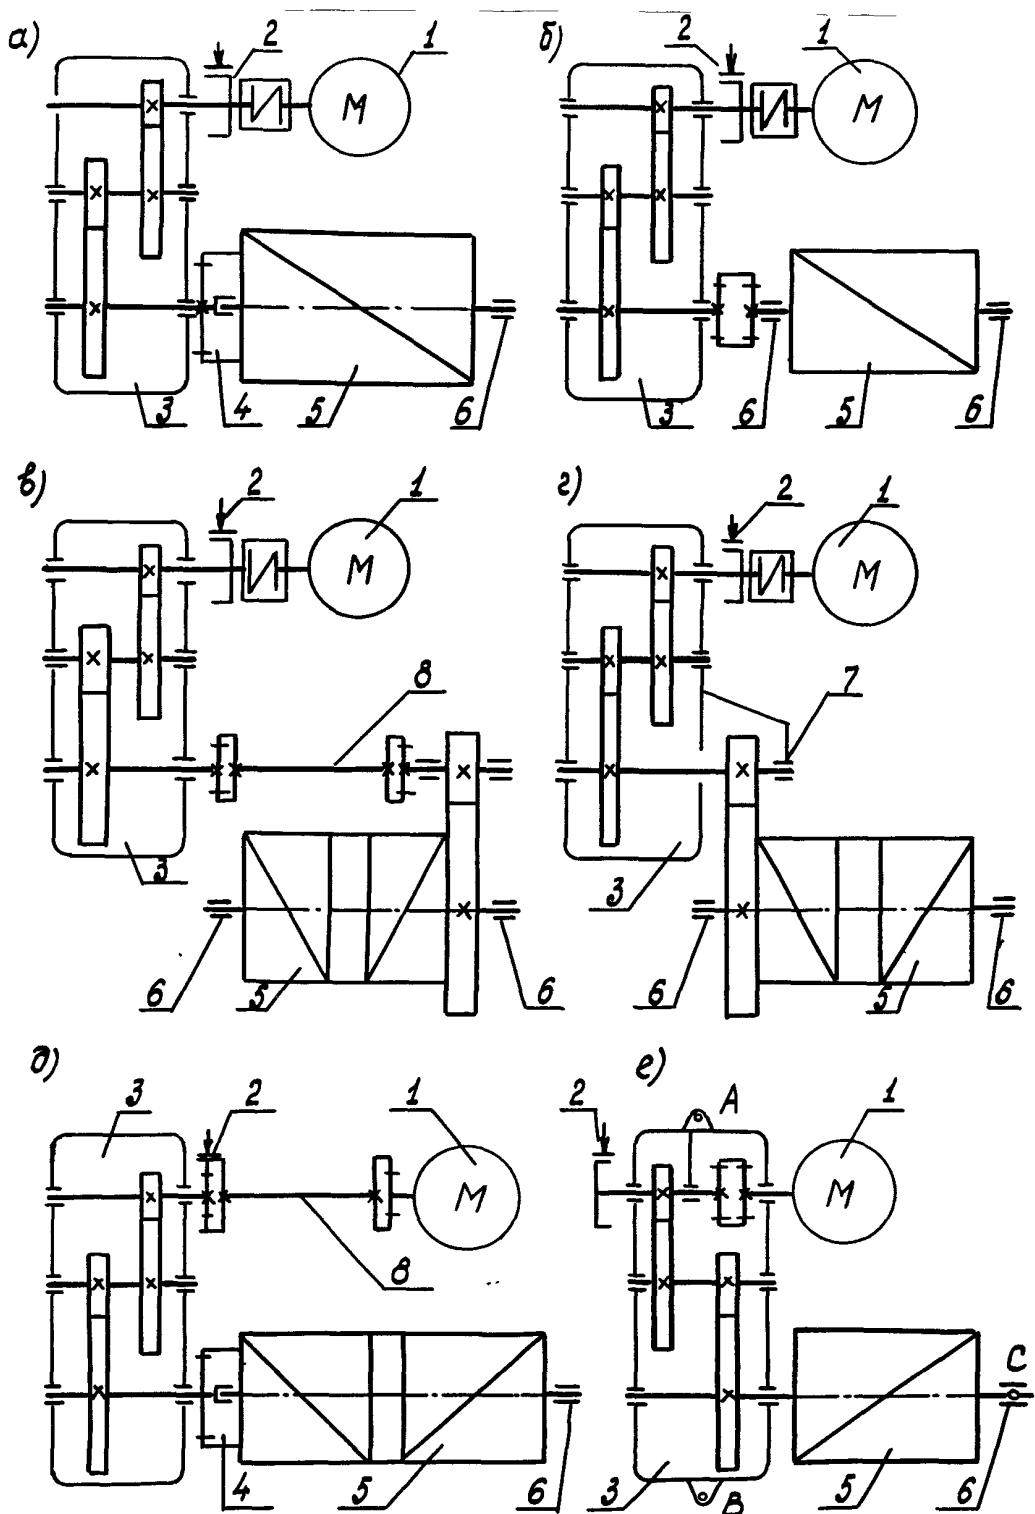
Основные типы механизмов подъема крюковых кранов: 1-двигатель, 2-тормоз, 3-редуктор, 4-зубчатая муфта, 5-барабан, 6-опора барабана
